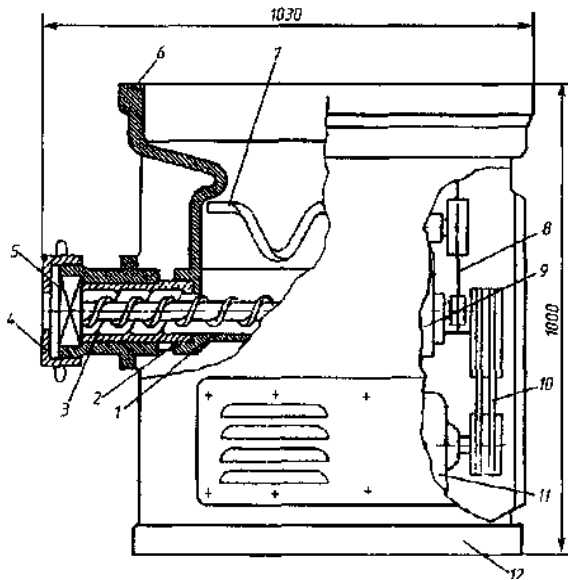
Вовчок ФМП-2-120: 1 - робочий шнек; 2 - циліндричний корпус; 3 - гільза; 4 - гайка накладна; 5 - ріжучий механізм; 6 - завантажувальна горловина; 7 - подавальна спіраль; 8 - ланцюгова передача; 9 - редуктор; 10 - клинопасова передача; 11 - електродвигун; 12 - станина
